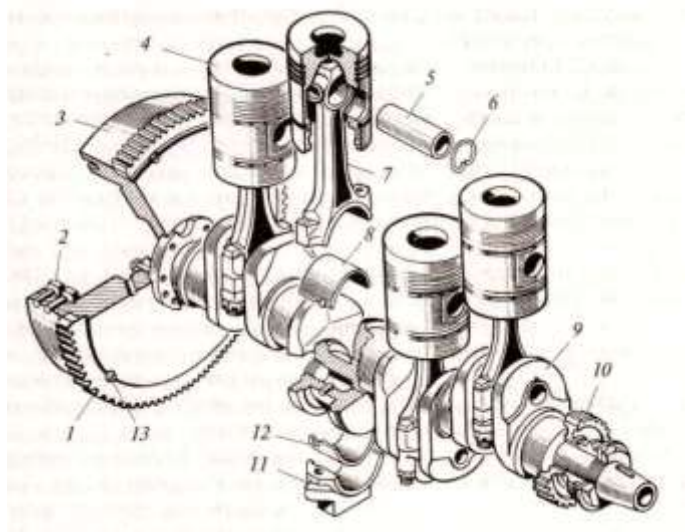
Кривошипно-шатунный механизм рядного двигателя:
